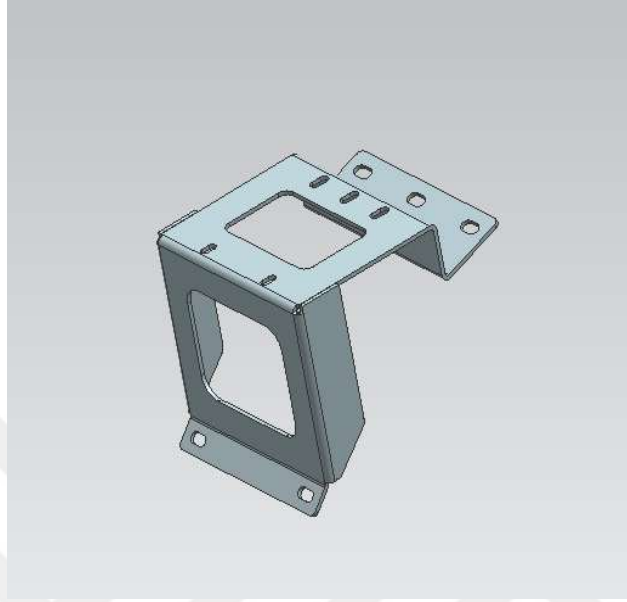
’te gösterilen Braket-4 tasarımında, bağlantı noktalarının rijitliğini artırmak ve yapısal dayanımı iyileştirmek amacıyla kenar bölgelerde flanş yapıları oluşturulmuş ve bu bölgeler uygun şekilde bükülerek desteklenmiştir.
